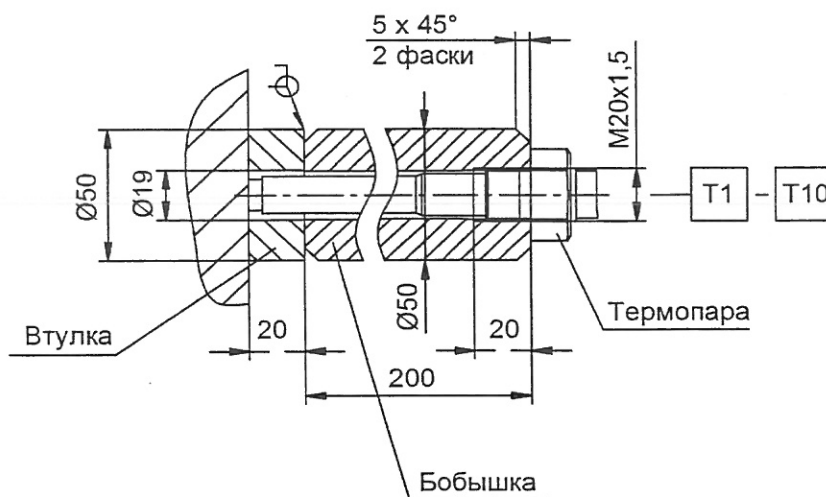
Штуцер для установки поверхностной термопары для реакторов Р-1/1, Р-1/2
